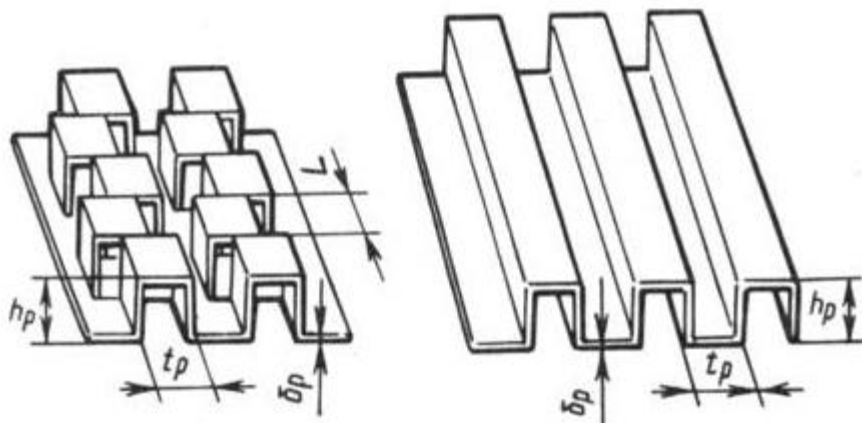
Насадка пластинчасто-ребристої поверхні:
